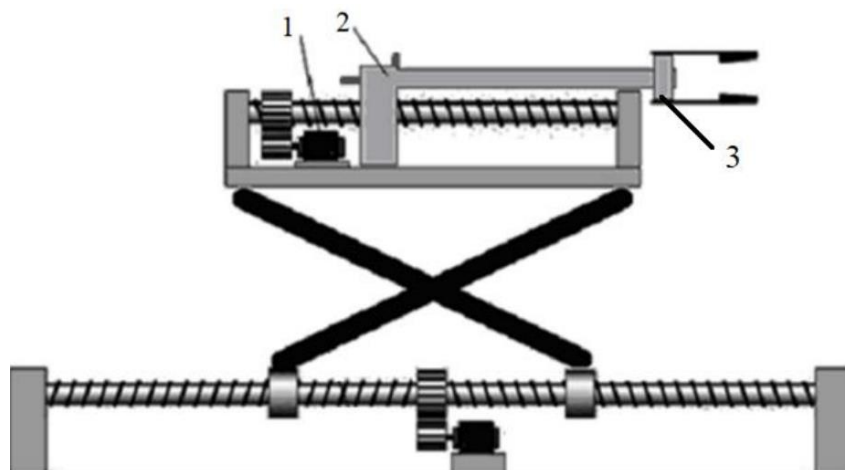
Загальний вигляд механізму переміщення заготовок
